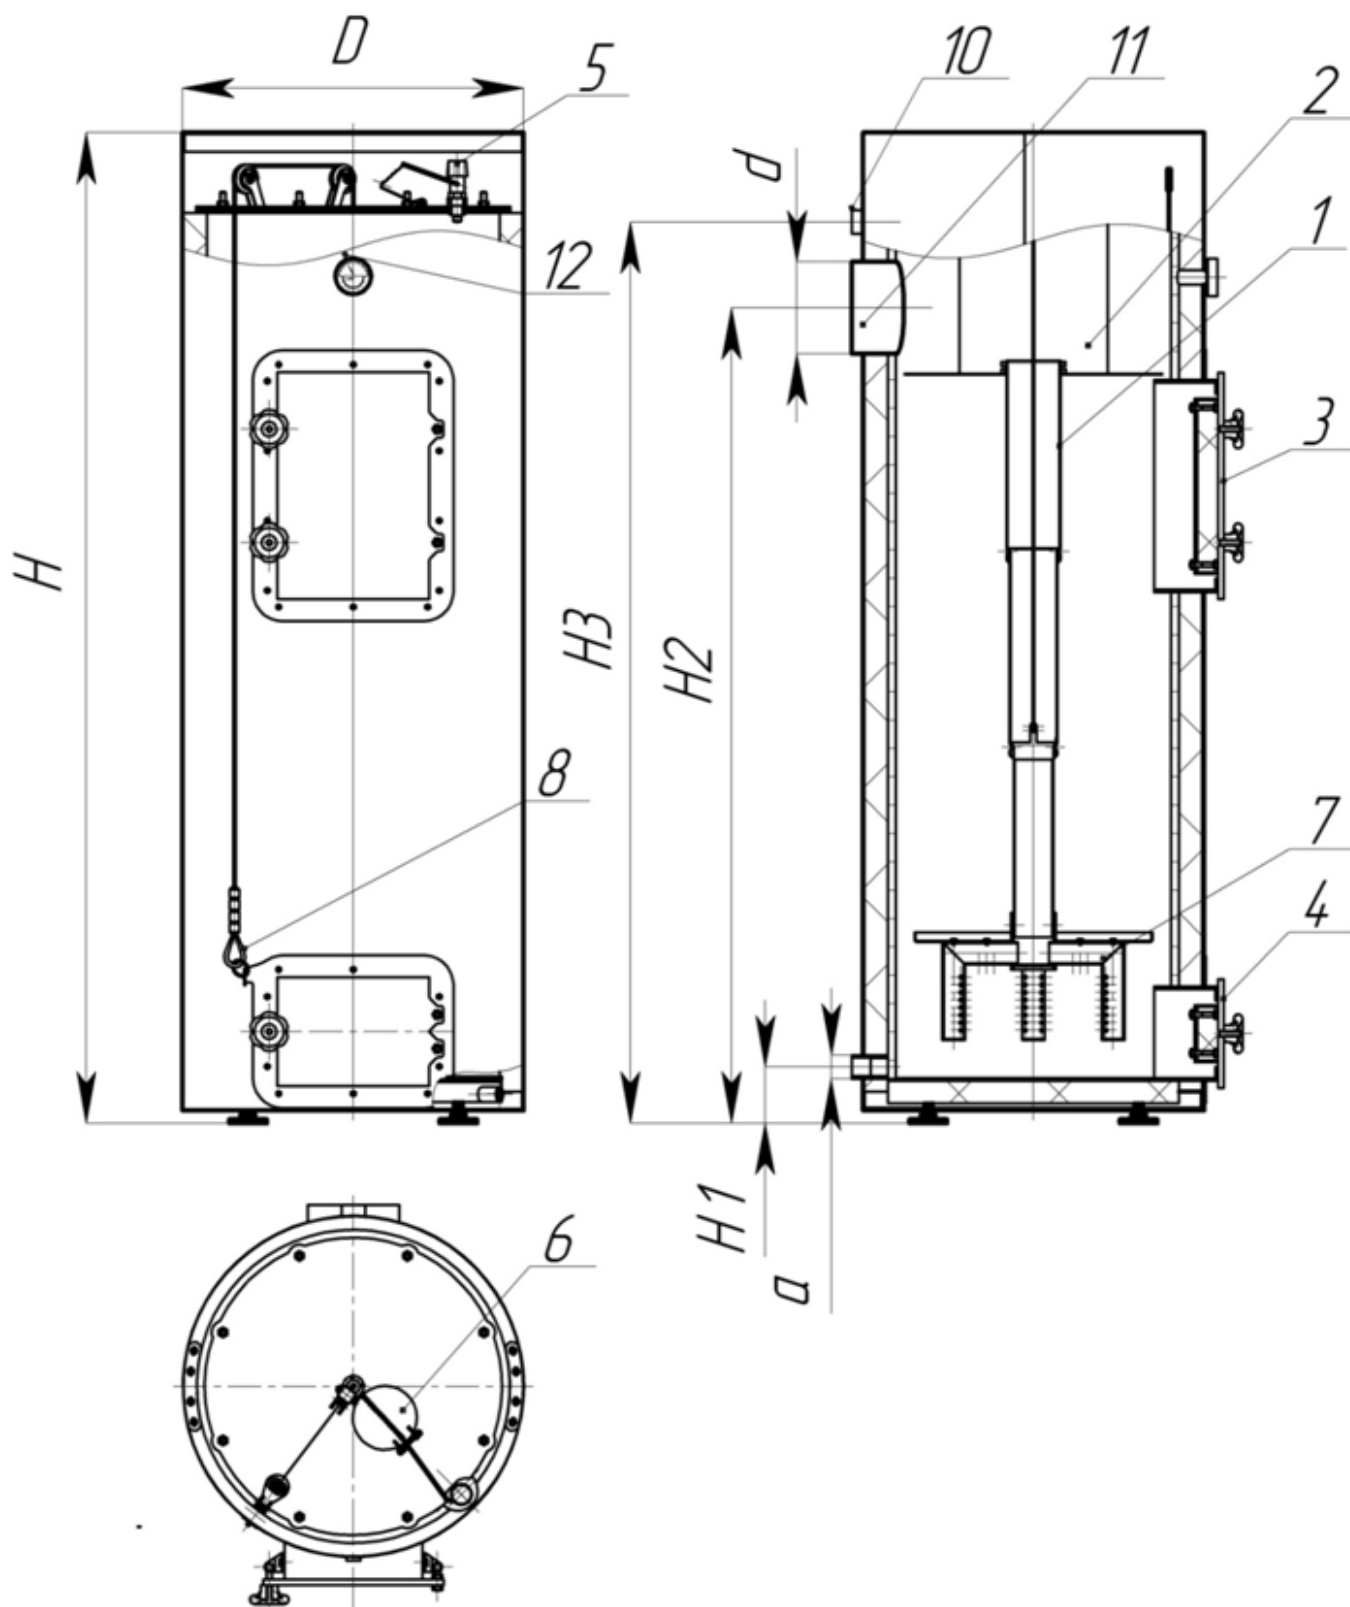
Габаритные и присоединительные размеры версии КВр-XX.
